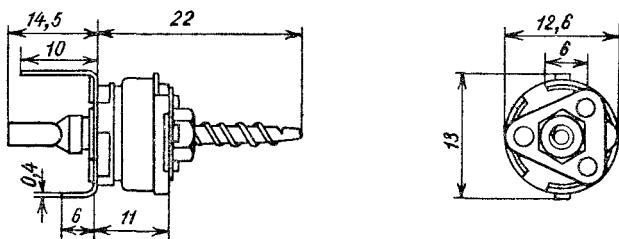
Цилиндрический тип подстроечного конденсатора фирмы «Муллард»; размеры в миллиметрах.
